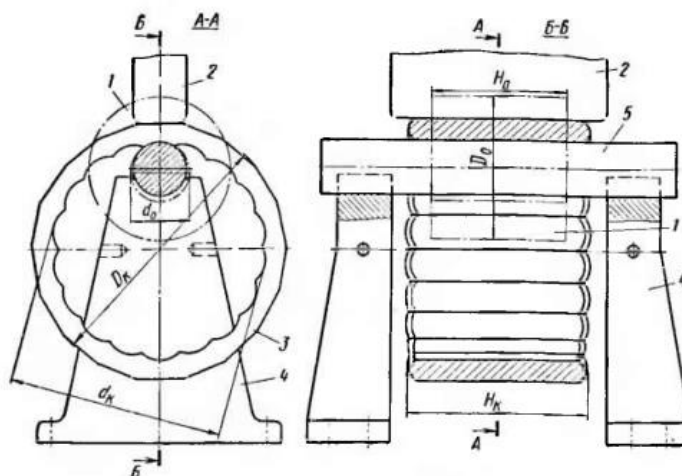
Схема процесу розкочування: 1 - прошита заготовка, 2 – вузький плоский бойок, 3 – кільце при розкочуванні, 4 – стійки, 5 – оправка
